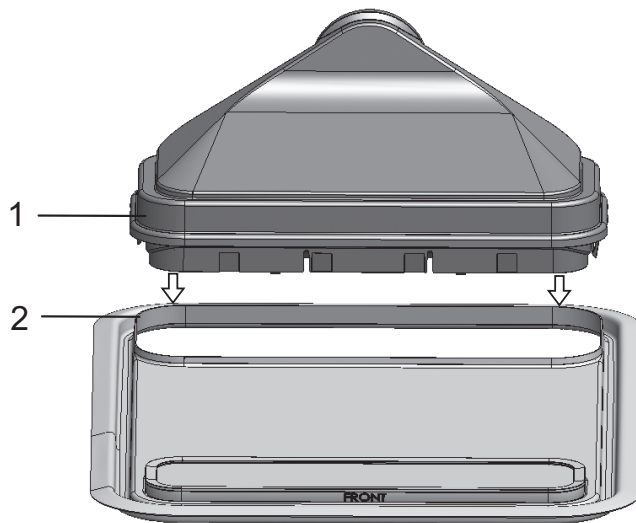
Poser le boîtier du filtre à air sur le couvercle du réservoir d'eau
